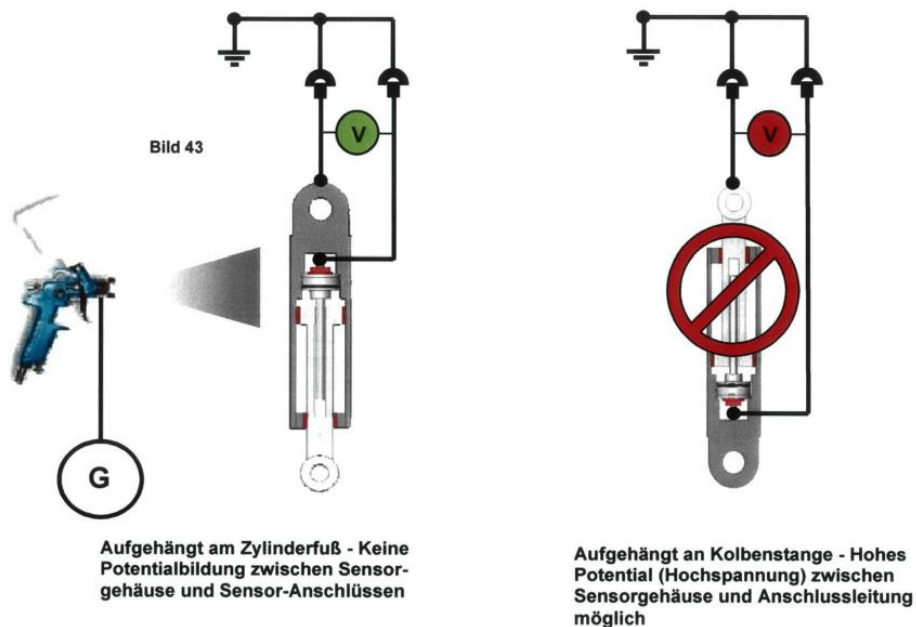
, Zylinderaufhängung mit Wegaufnehmer
